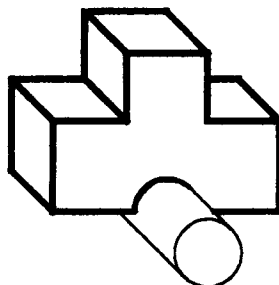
Получение выемки рассечением предмета цилиндрической поверхностью
